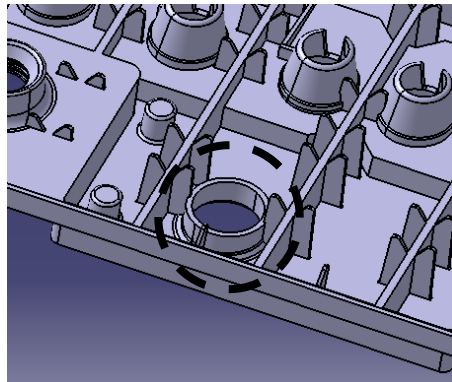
Vista isométrica del hoyo de carga, diseño original tapa BCI 42
